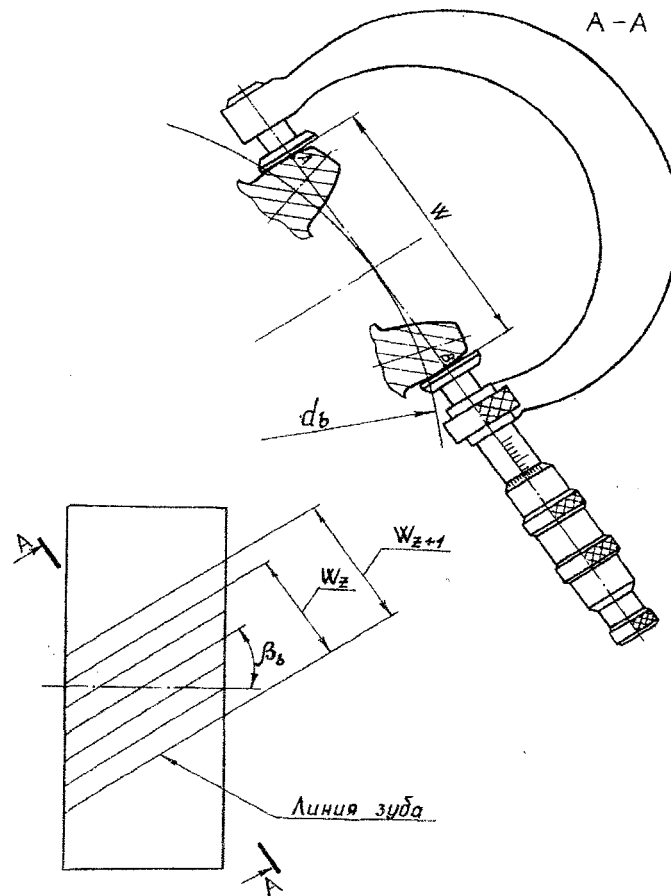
Схема измерения длины общей нормали косозубого колеса
